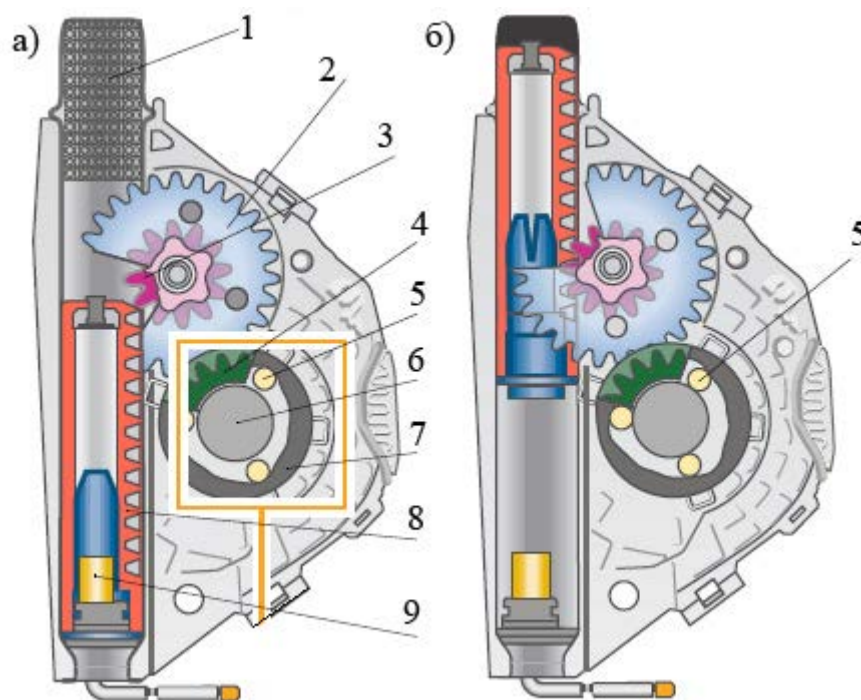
Реечный преднатяжитель ремня безопасности: 1 – демпфер; 2, 3, 4 – шестерни; 5 – ролик; 6 – торсионный вал; 7 – наружное кольцо обгонной муфты; 8 – поршень с зубчатой рейкой; 9 – пиропатрон; а – исходное положение; б – завершение натяжения ремня
